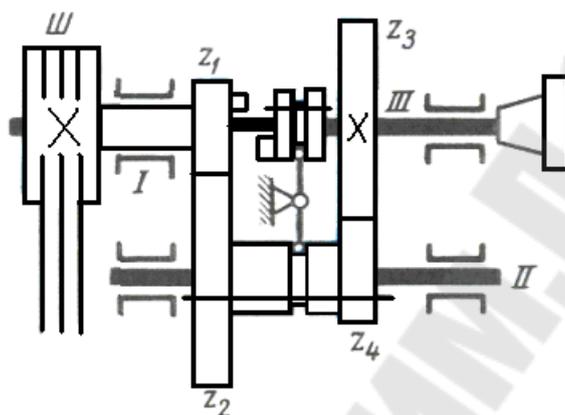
Схема шестеренчатой коробки скоростей с перебором
